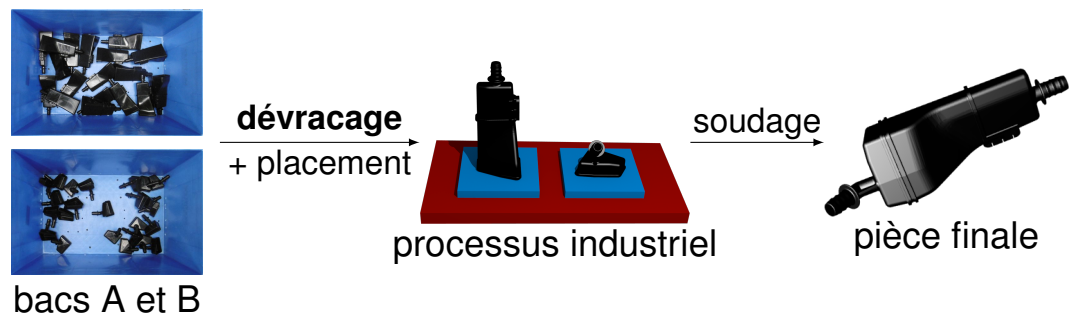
Détails de l'injection et de l'assemblage par soudage d'une pièce en plastique injecté.
